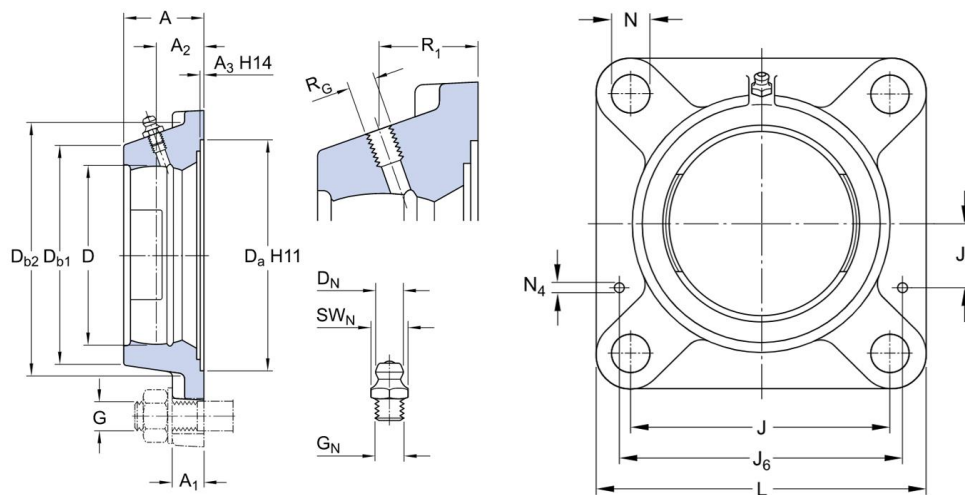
Soporte de pestaña cuadrado para rodamientos Y SKF (Fuente: <https://www.skf.com/cl/products/bearings-units-housings/bearing-units/ball-bearing-units/y-bearing-flanged-units/square-flanged-housings-for-y-brgs/index.html?designation=FYJ%20520>)
